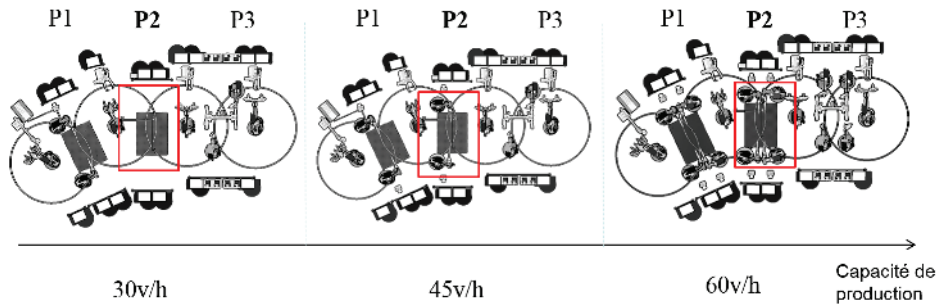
Configurations d'une ligne d'assemblage de plancher central
